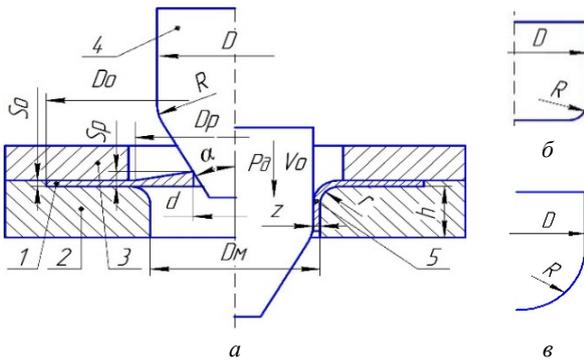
Схема відборткування профільованої заготовки конусним пуансоном та форми пуансонів
